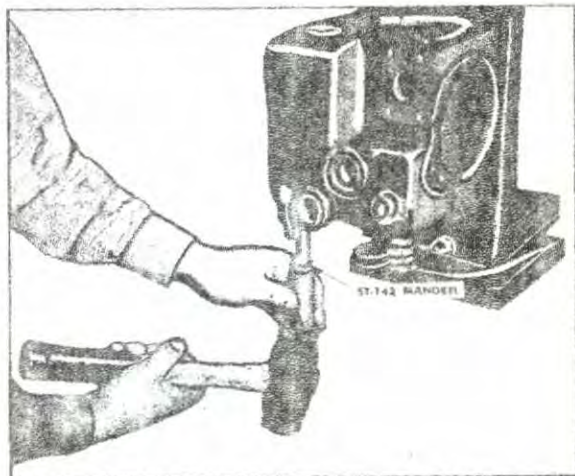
Instalación del cojinete de la excéntrica de control a mano.
